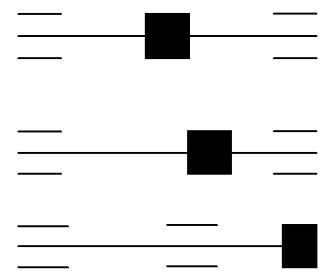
Схеми розташування коліс відносно опор вала
